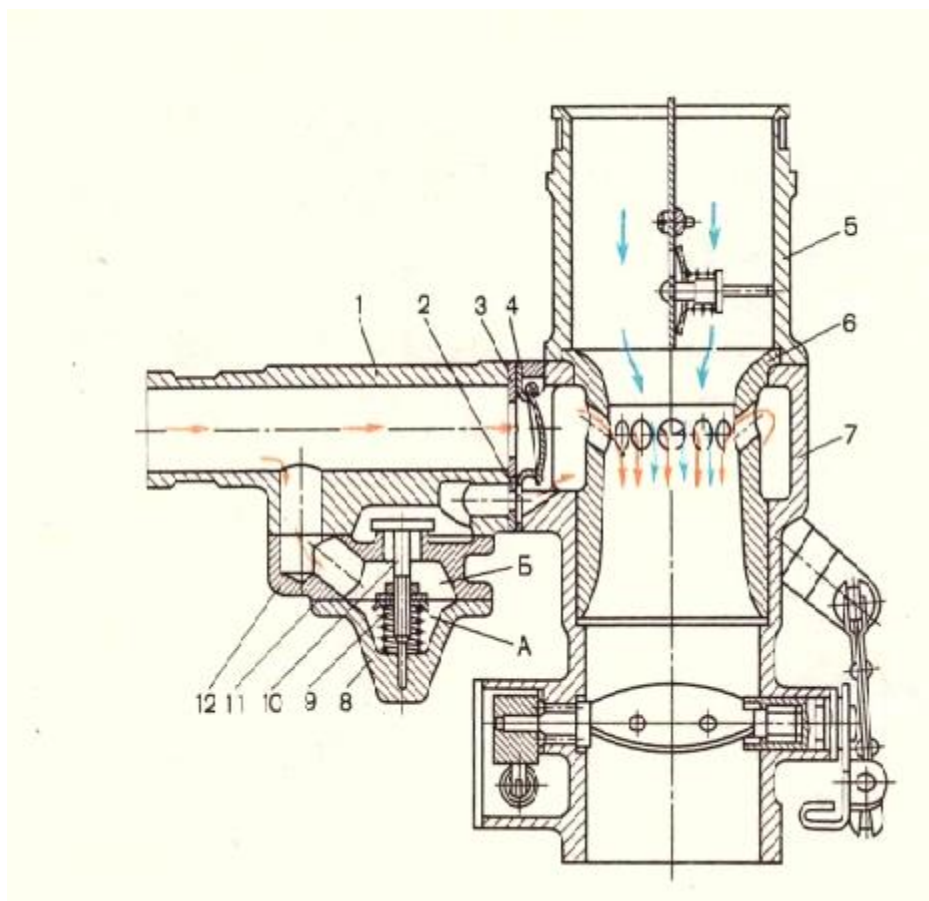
Газовоздушный смеситель автомобильного типа:
